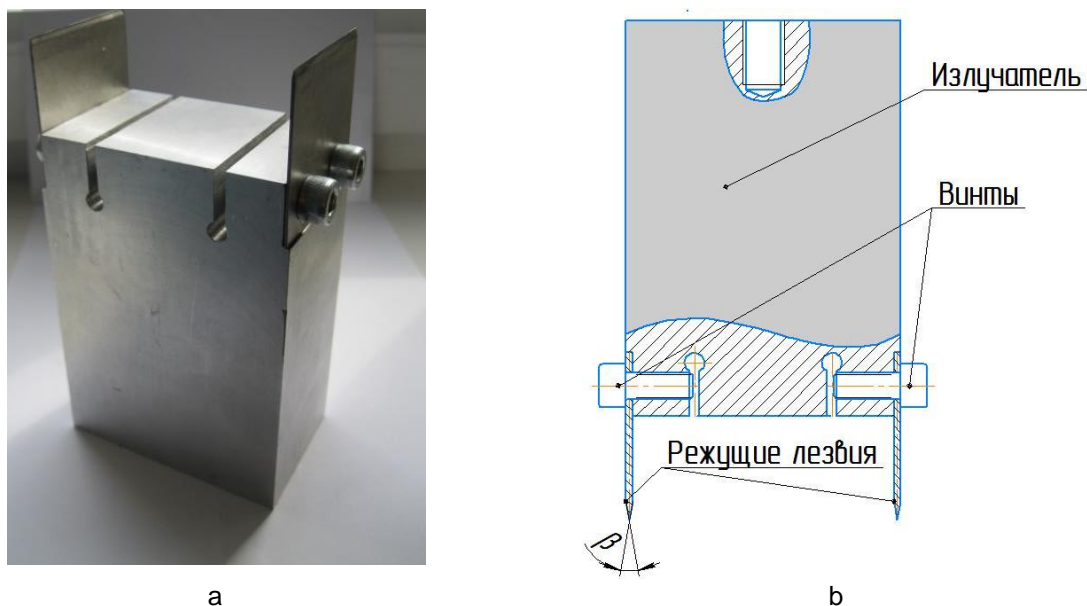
Ультразвуковое режущее устройство; а - фотография устройства, б – чертеж устройства
